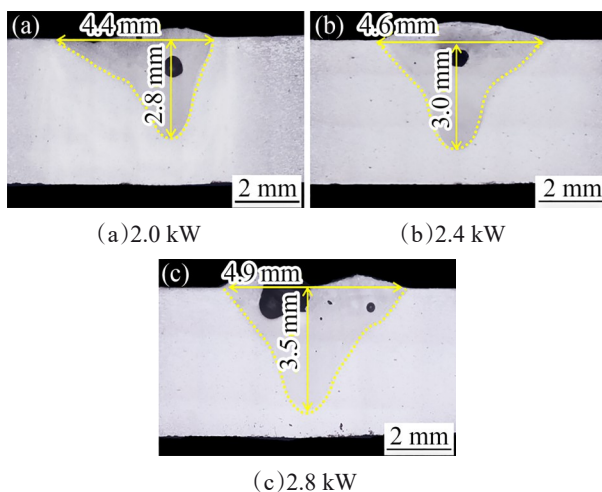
为不同激光功率下 Al-7Mg-3Zn 合金激光-TIG 焊焊缝横截面形貌。随激光功率从 2.0 kW 增大到 2.8 kW,熔宽从 4.4 mm 增大到 4.9 mm,熔深从 2.8 mm 增大到 3.5 mm。此外,各激光功率下的接头均存在气孔缺陷,当激光功率增至 2.8 kW 时,焊缝内出现大尺寸不规则气孔,局部气孔尺寸达到 0.4 mm 以上。图 4 为焊缝深宽比与横截面面积随激光功率
